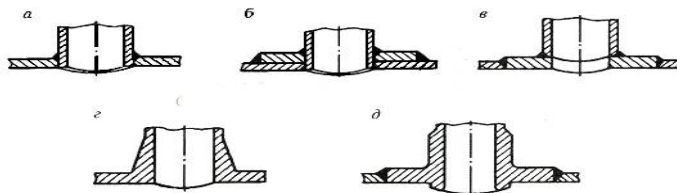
Укрепление круговых вырезов корпусов аппаратов: а – примыкающим патрубком; б – примыкающим патрубком и накладкой; в – сварным кольцом и примыкающим патрубком; г – примыкающим патрубком с коническим переходом; д – сквозным патрубком и сварным кольцом
